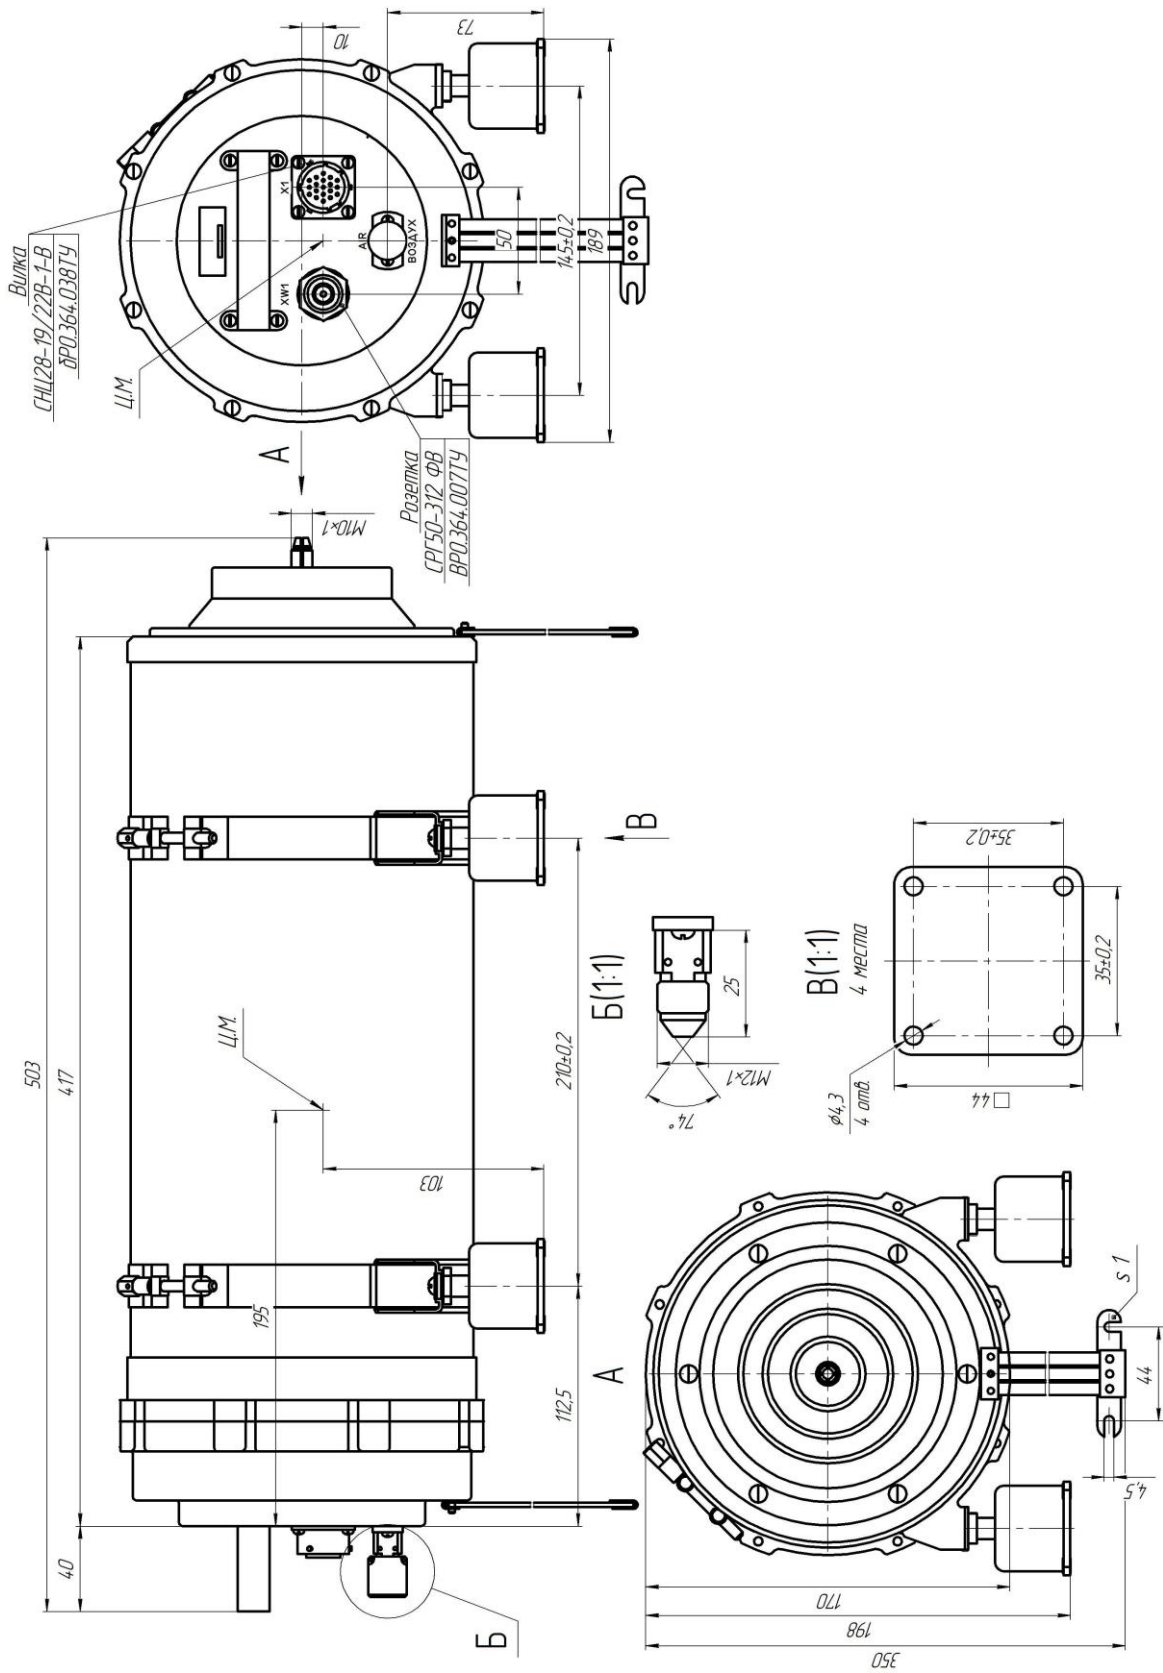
Габаритный чертёж блока Б5А1-ПрП
